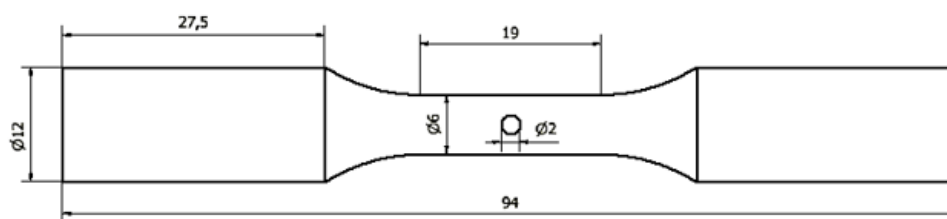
Geometria dos provetes, com furo passante, dimensões em milímetros.
